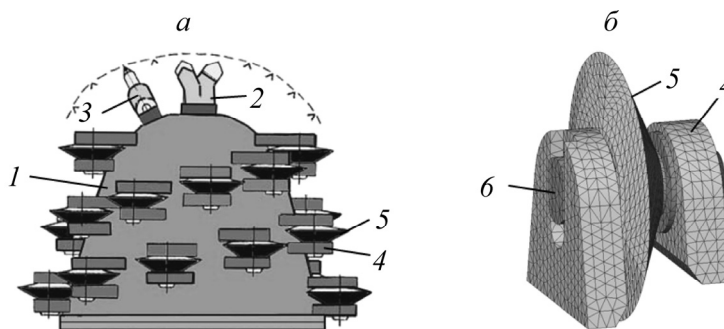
Экспериментальная коронка с узлами крепления дискового инструмента: а — конструкция; б — конечно-элементная модель двухопорного узла крепления; 1 — коронка; 2 — забурник; 3 — резец; 4 — кронштейн; 5 — диск; 6 — ось
